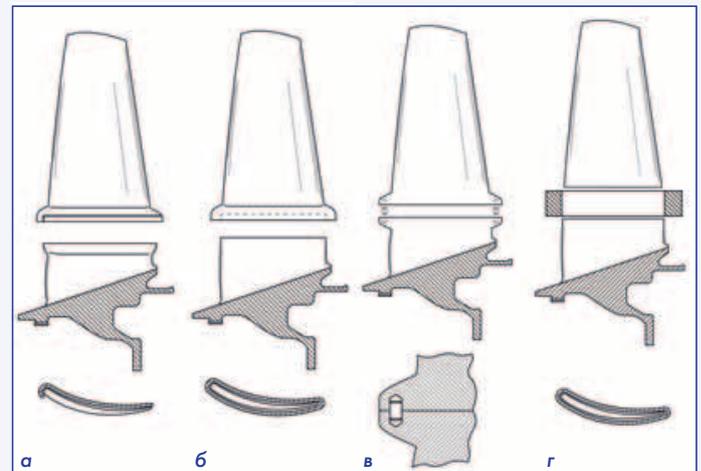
Метод ремонта монокопел, имеющих укороченные лопатки: а) сварка лопатки "в колодец", неполное перекрытие; б) сварка лопатки "в колодец", полное перекрытие; в) сварка в кольце; г) фиксация лопатки штифтами
